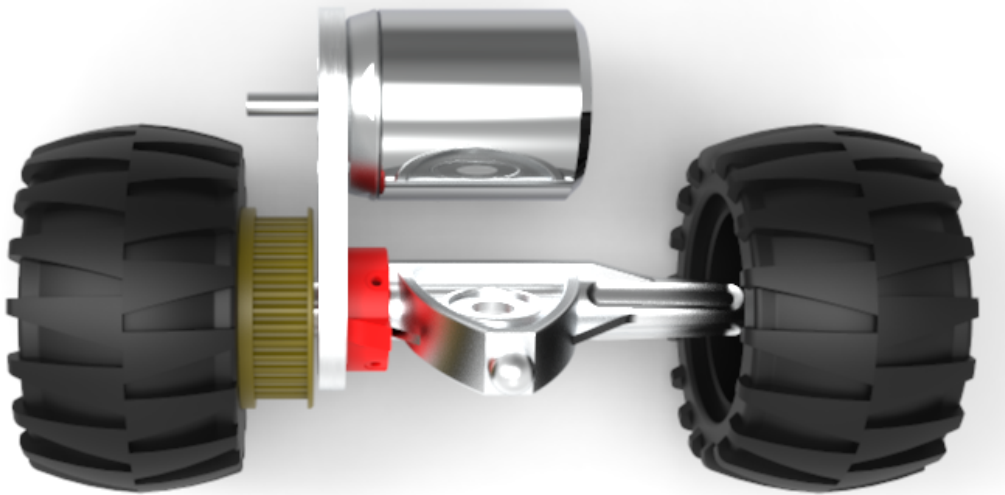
Ensamblaje del soporte del motor sobre la percha.
